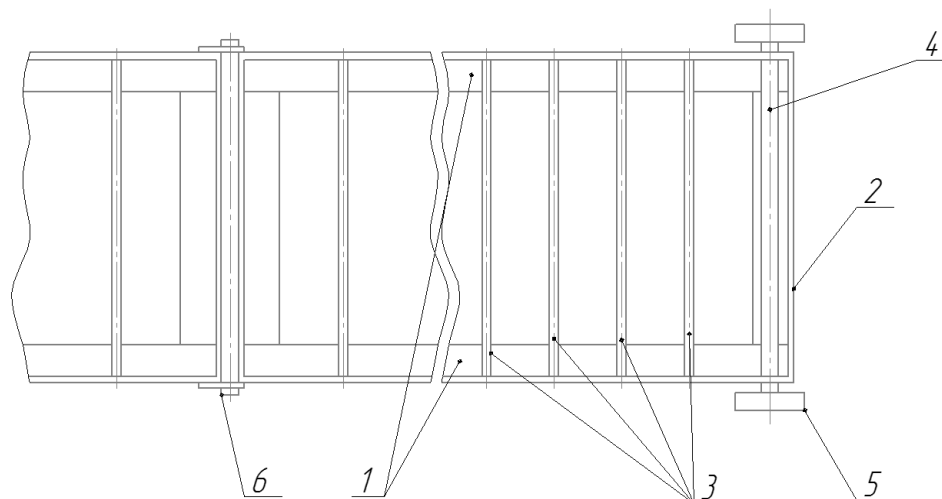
Секция сварная конструкции для сушки пожарных рукавов
